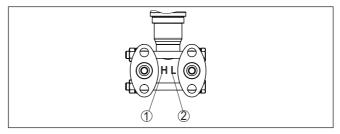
Kennzeichnung für Hoch-/Niederdruckseite an der Prozessbaugruppe
